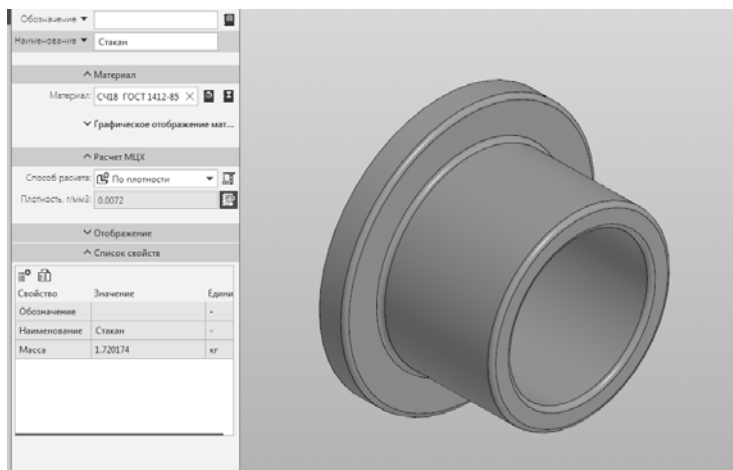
Заготовка детали «Стакан» и ее свойства
